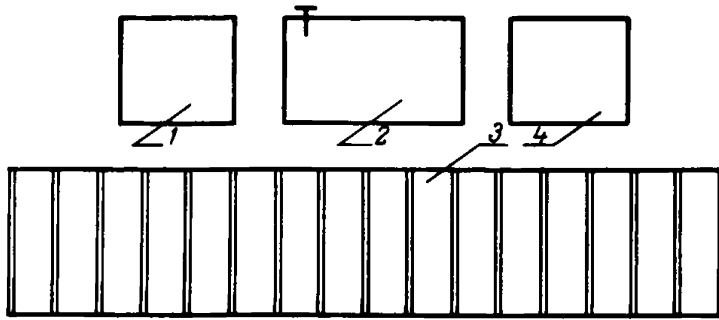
Типовая схема планировки рабочего места разборки гидромеханической передачи:
